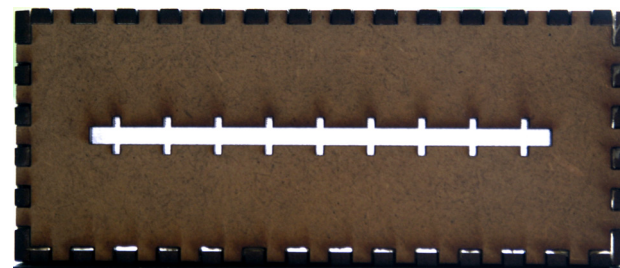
Udskåret front med rille på 8 cm og 9 tvær riller.
